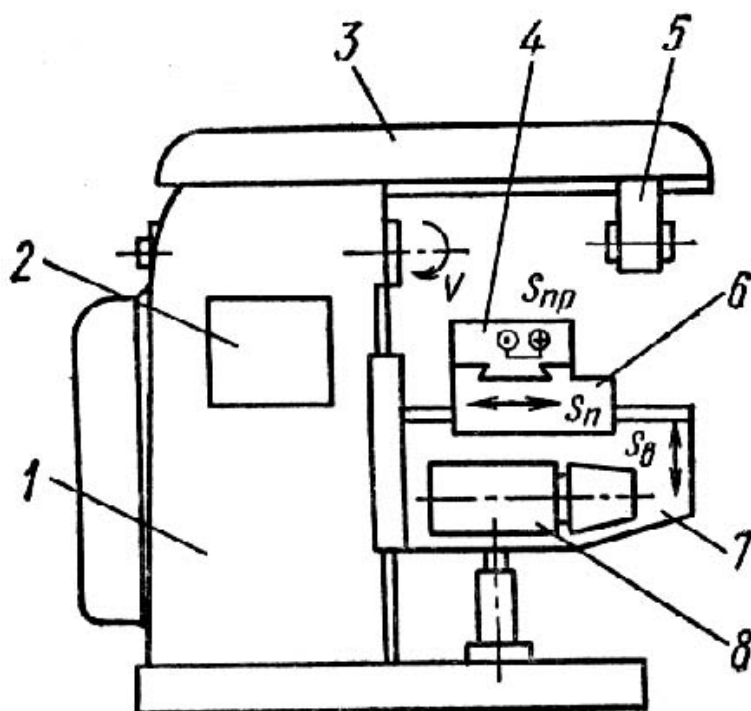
Общий вид горизонтально-фрезерного станка:
